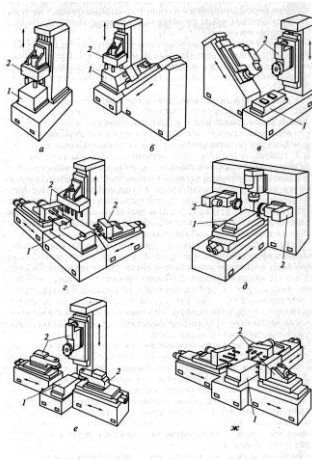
Типові компонування однопозиційних агрегатних верстатів зі стаціонарним пристроєм для обробки заготовки з одного (а), двох (б, в) і трьох (г-ж) сторін: 1 - стаціонарні пристрої; 2 - силові вузли
